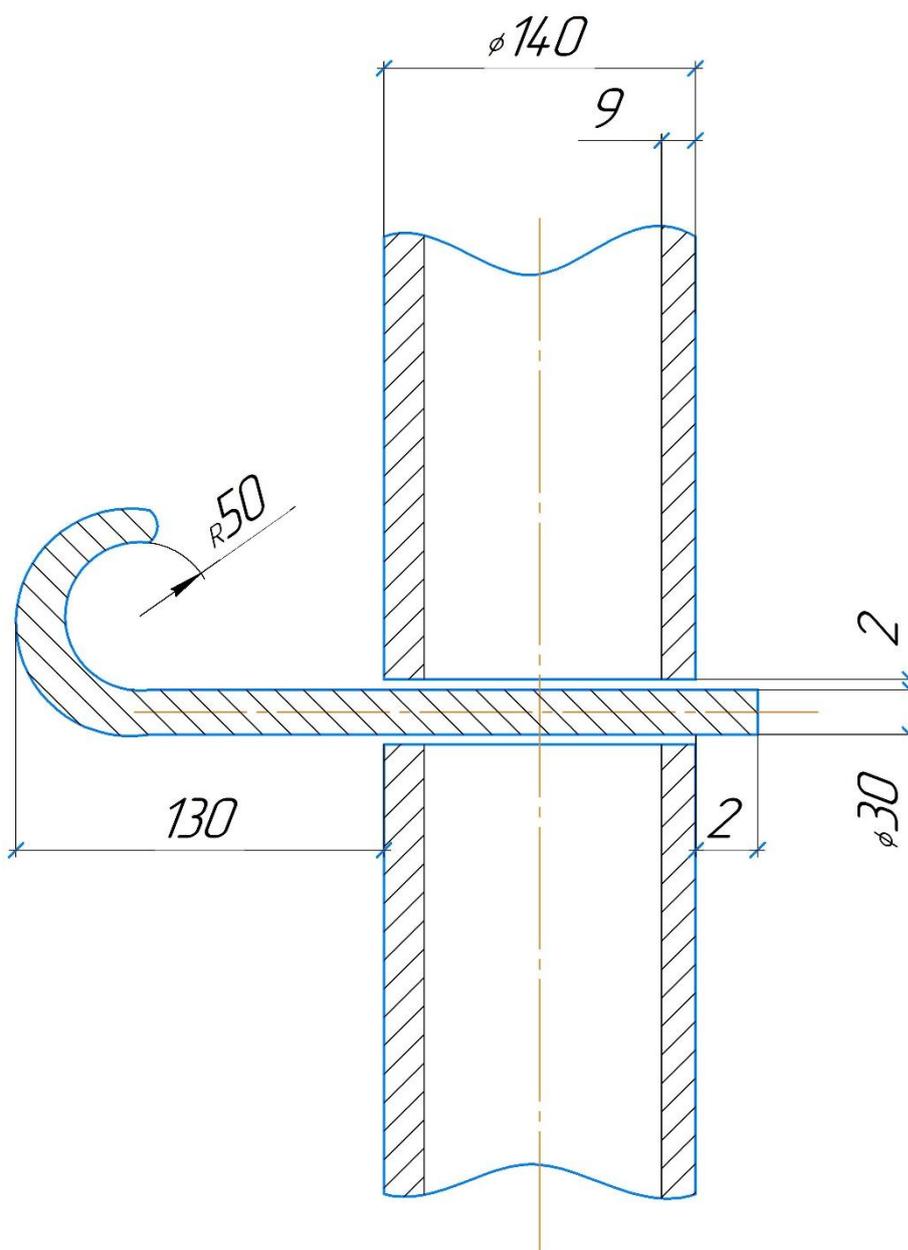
Труба с вставленным крюком перед сваркой
